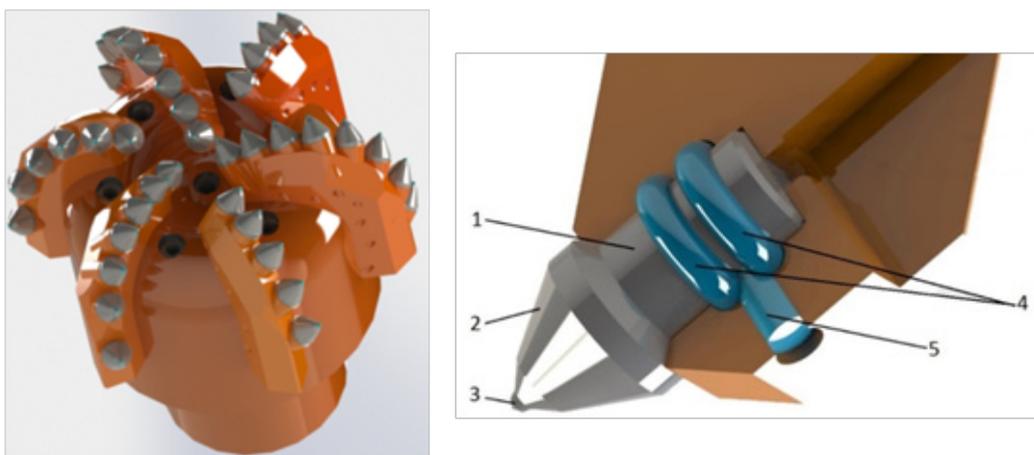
Лопатное долото с поворотными резцами: 1 – хвостовик резца; 2 – головка резца; 3 – твердосплавный наконечник; 4 – полимерный материал; 5 – отверстие для заливки
